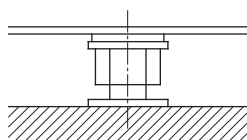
Vis de réglage de niveau sur la surface de fondation
